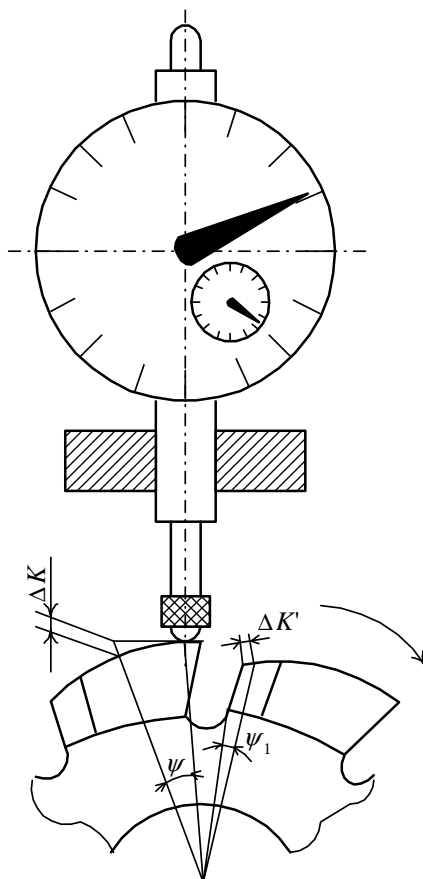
Схема вимірювання величини падіння затилку фрези
